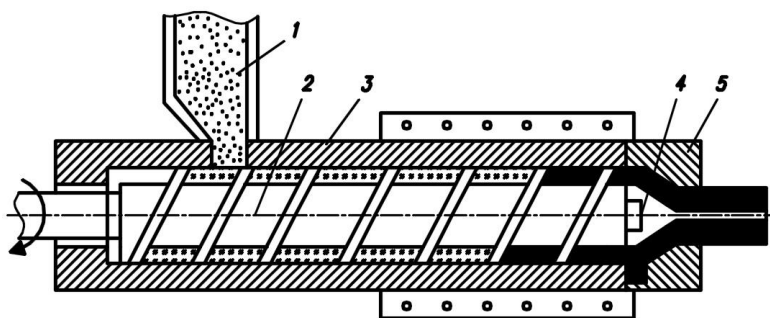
Схема получения деталей из термопластичных полимеров экструзией:
